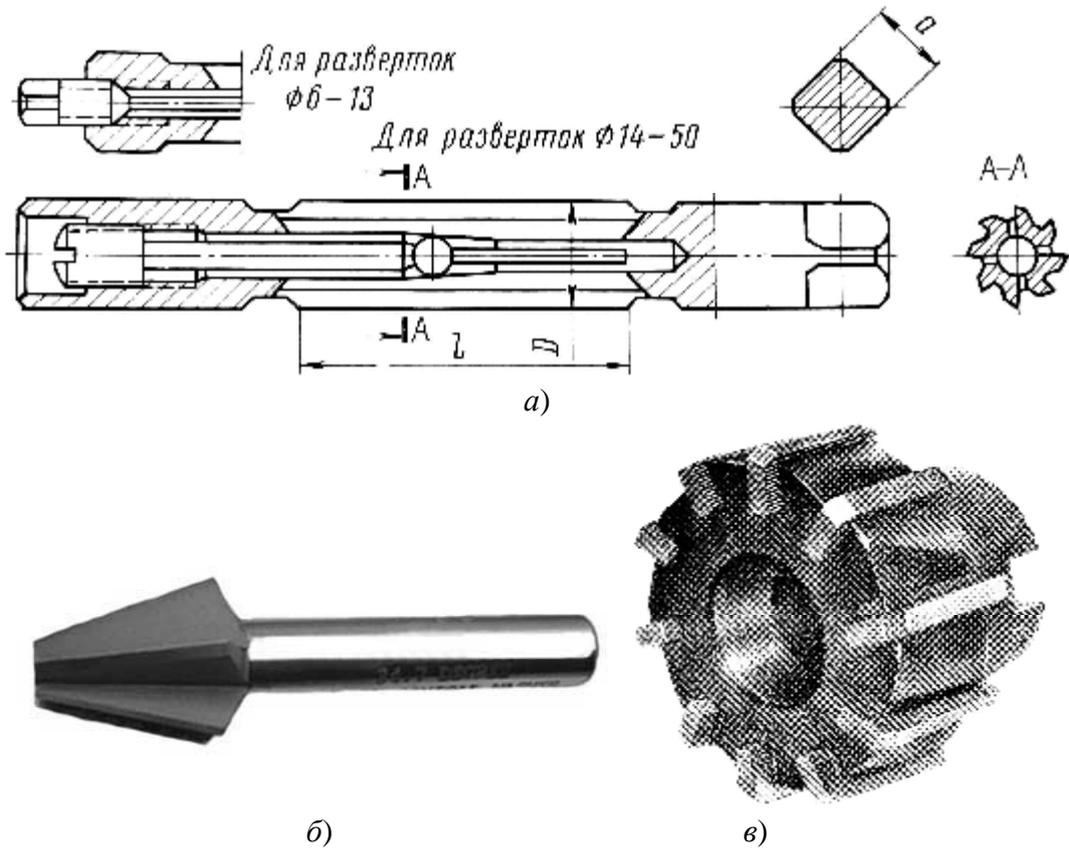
Развертки: а – ручная разжимная; б – коническая; в – машинная насадная со вставными ножами из быстрорежущей стали
